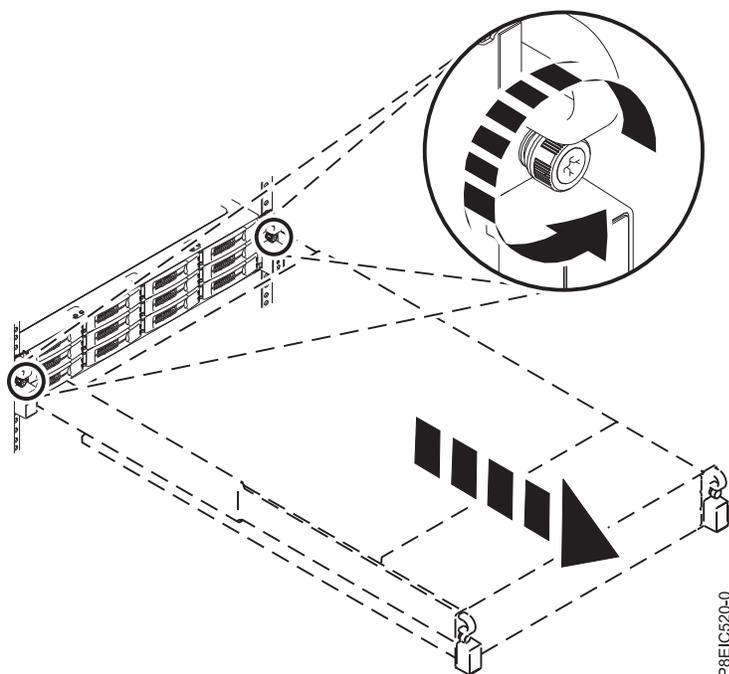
Removendo os parafusos frontais e removendo o sistema do rack
